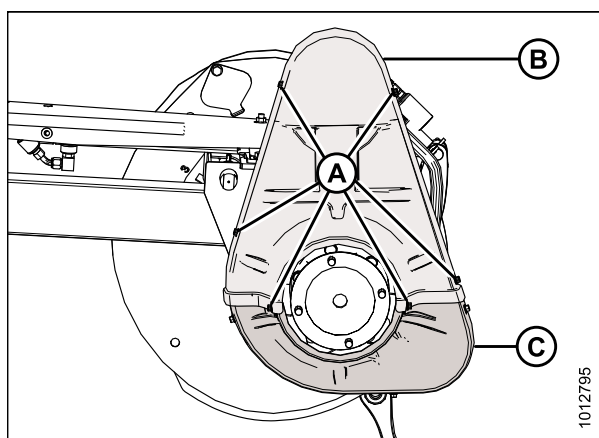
Крышка привода — сдвоенное мотовило
